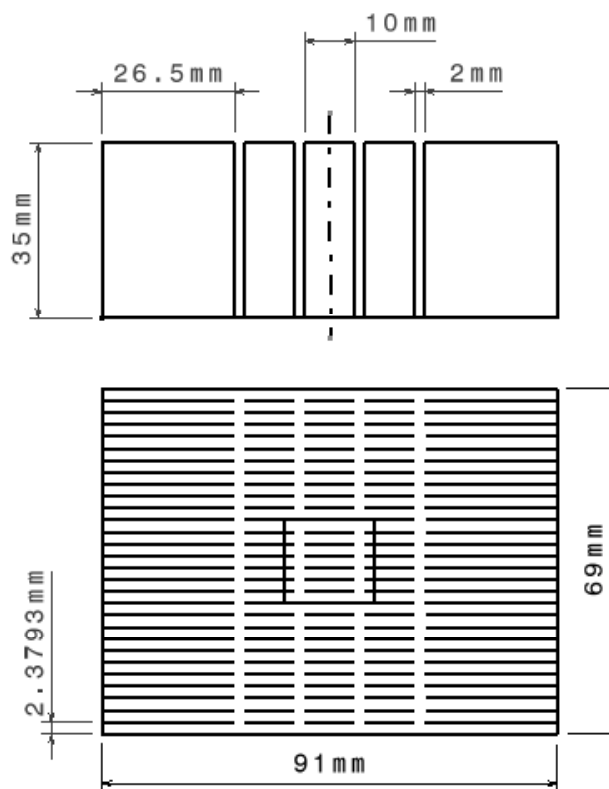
Dimensões finais do dissipador 11-P4ES-01.
